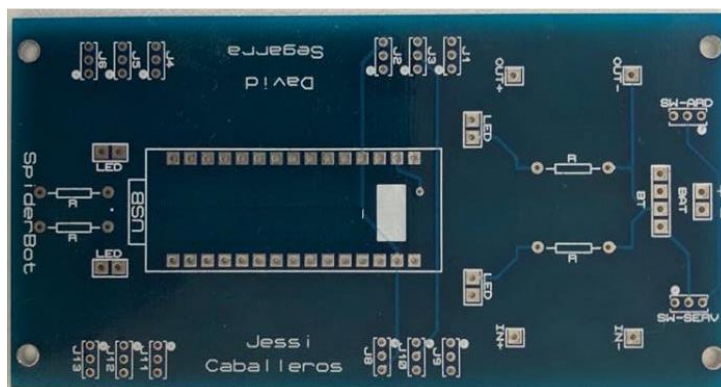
PCB final del Robot Cuadrúpedo SpiderBot
